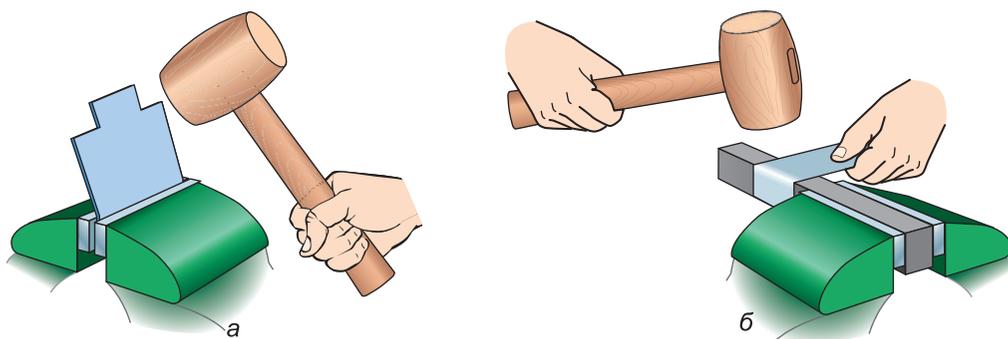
Гнутьё заготовок из тонколистового металла: а – в тисках; б – на оправке
